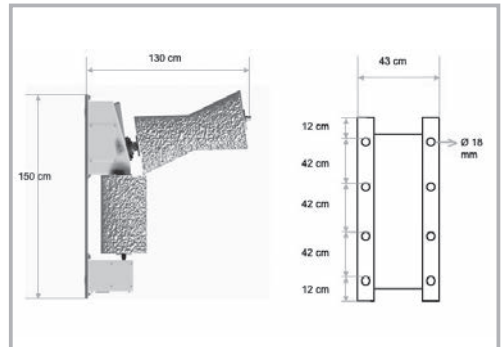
RotaBrush Twin: Montiert mit Installationsmaßen
